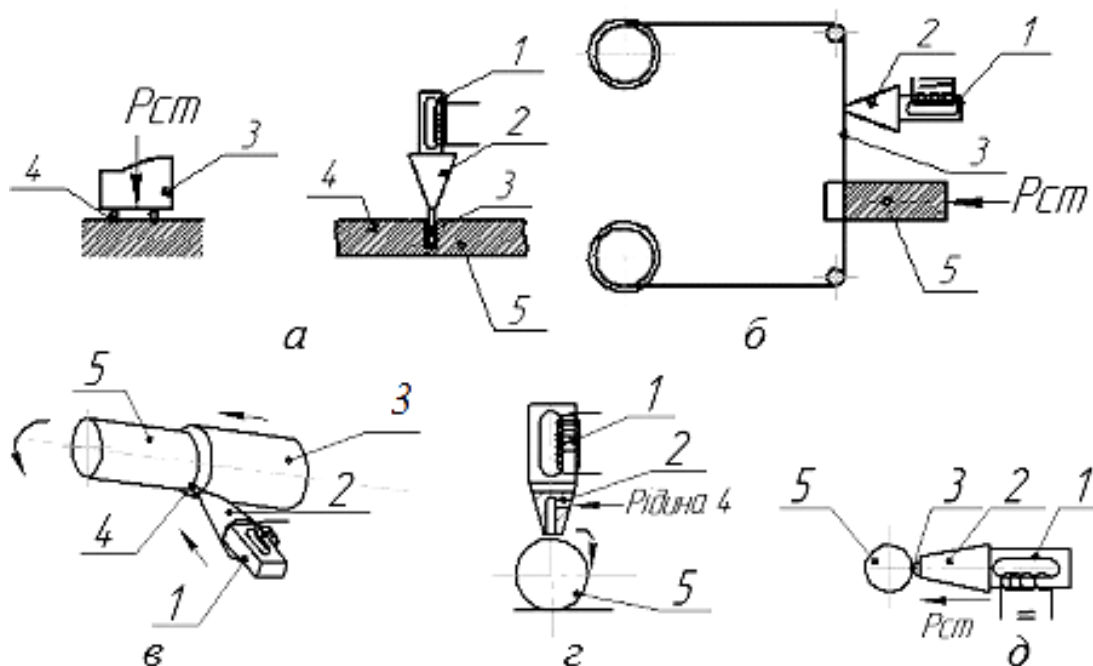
Схеми розмірної ультразвукової обробки заготовок
